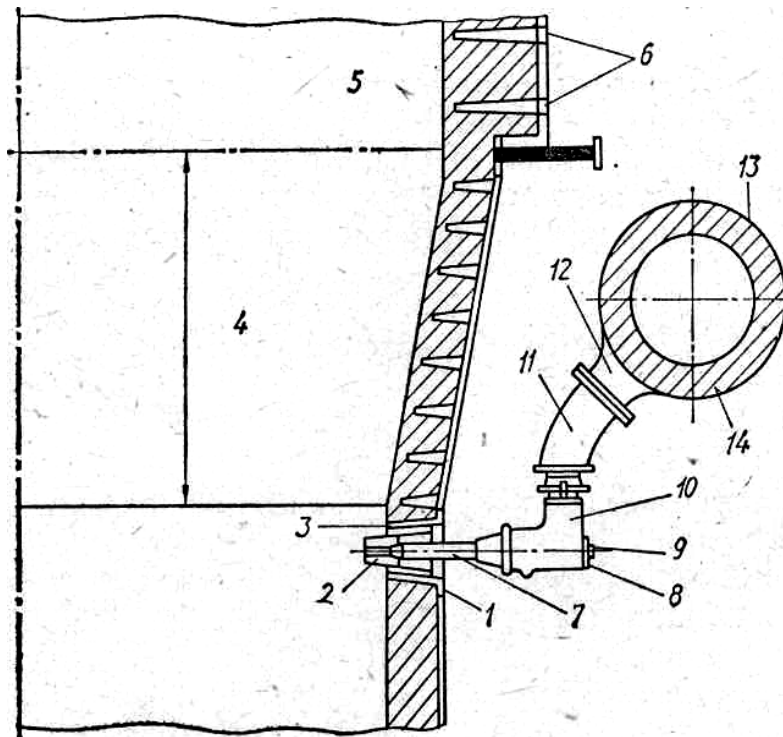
Section through tuyere opening Розріз по осі повітряної фурми
